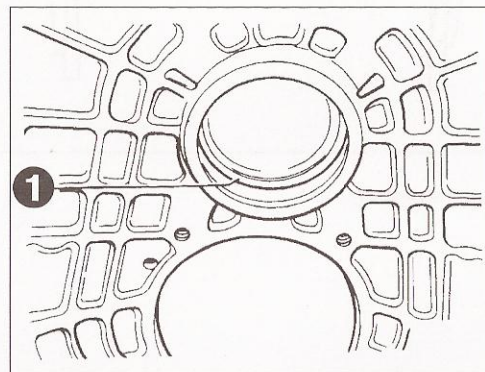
Установка регулировочного кольца (поз. 1) промежуточного вала.
